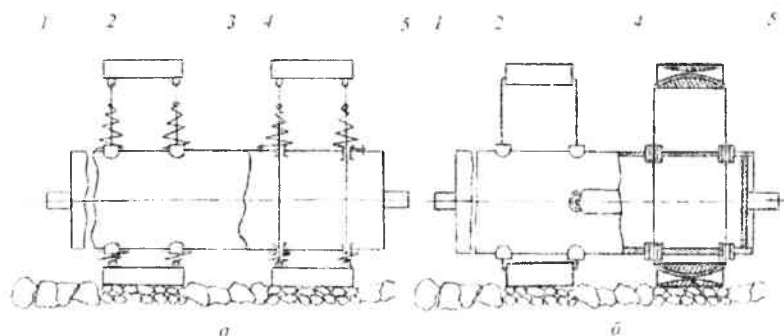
Ротационный рабочий орган с цилиндрическими рабочими элементами на парных (а) и кольцеобразных (б) гибких держателях:
